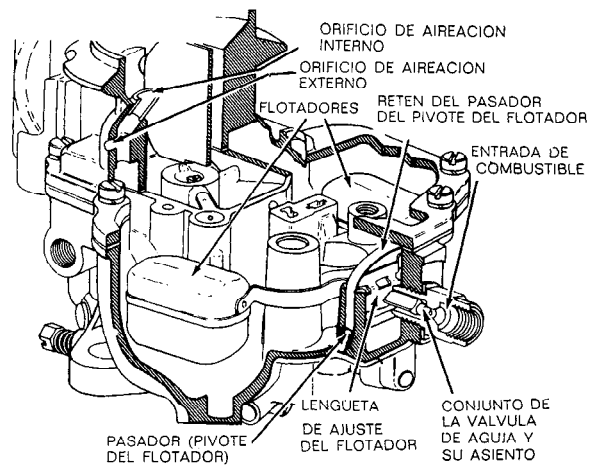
Corte parcial de un carburador, mostrando el circuito de flotador (American Motors Corporation).
